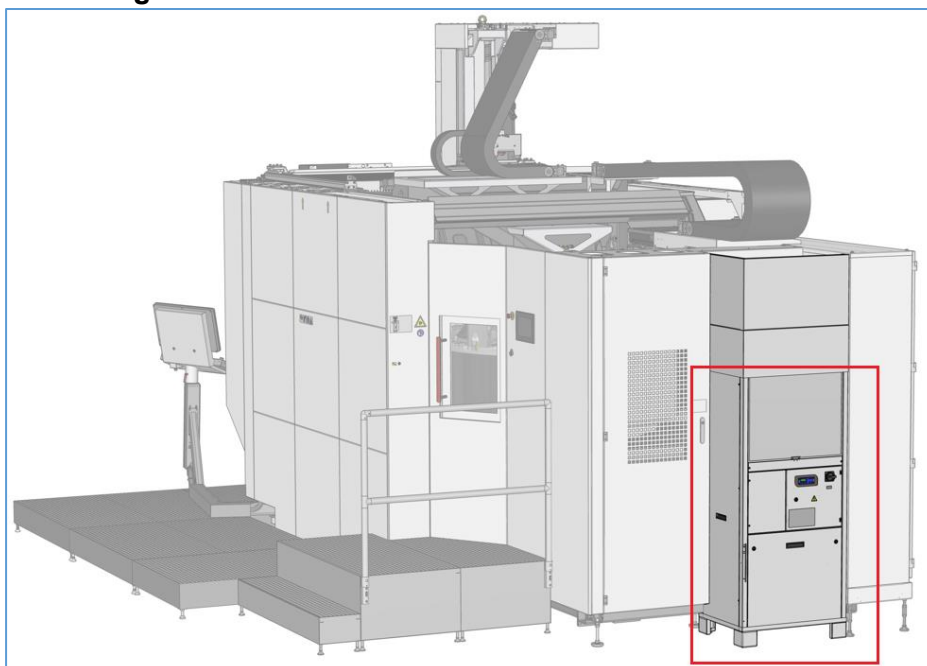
CNC-Werkzeugmaschine und einem Chiller (rot) für die Kühlung der WZM in Seitenmontage.
